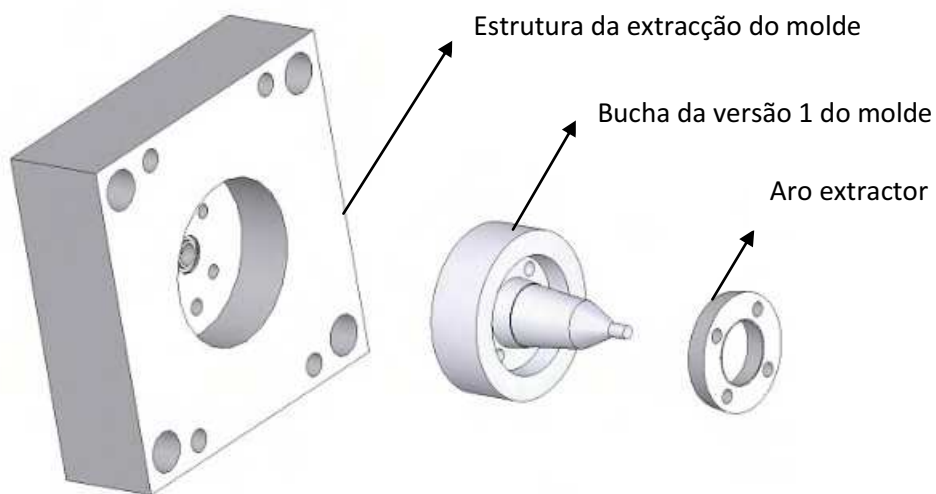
Componentes do molde – Bucha, chapa e aro extractor
